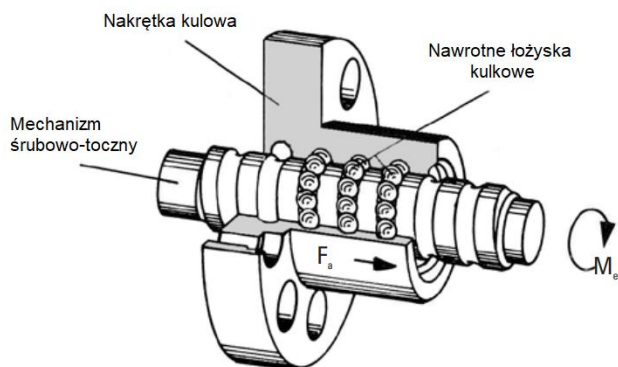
Widok po skosie obrazujący element mechanizmu śrubowo-tocznego – uproszczony silnik podnoszący górną część robota.
